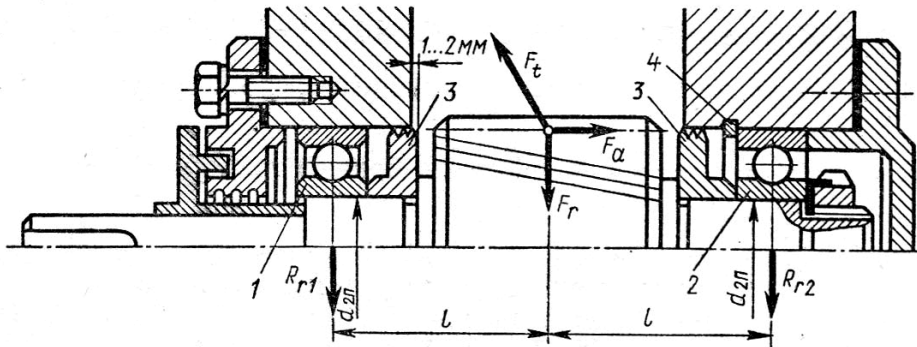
Опоры вала цилиндрического косозубого колеса при  $e \leq 0,35$
